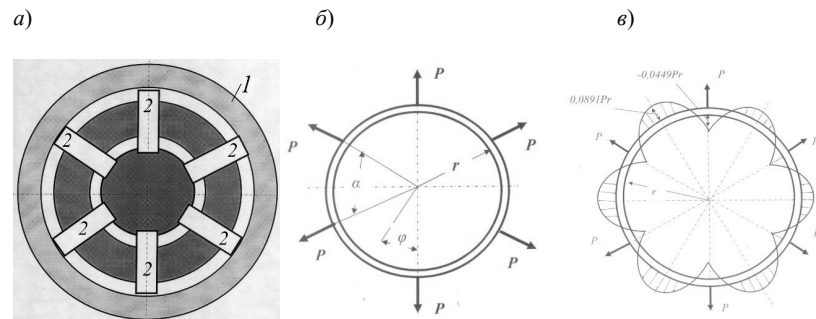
Схемы нагружения кольцевой заготовки 6-ю равномерно распределенными радиальными усилиями: а – схема расположения стабилизируемого изделия I и плунжеров 2; б – схема нагружения кольца радиальными силами P ; в – эпюры изгибающего момента
